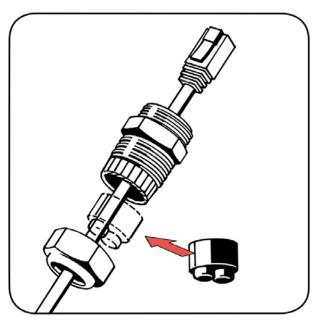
Kabelführung durch Kabelverschraubungen
